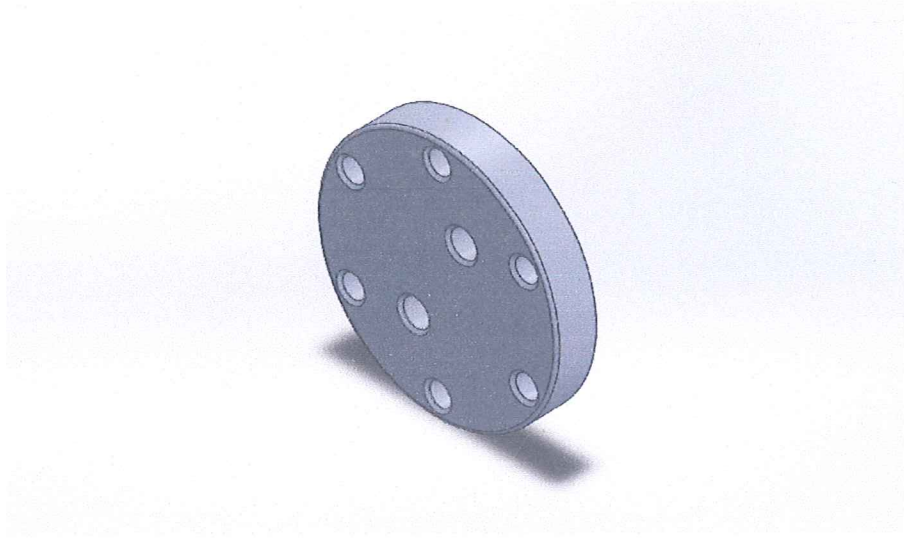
Kompresör piston gövde solidworks 3 boyutlu modelleme
